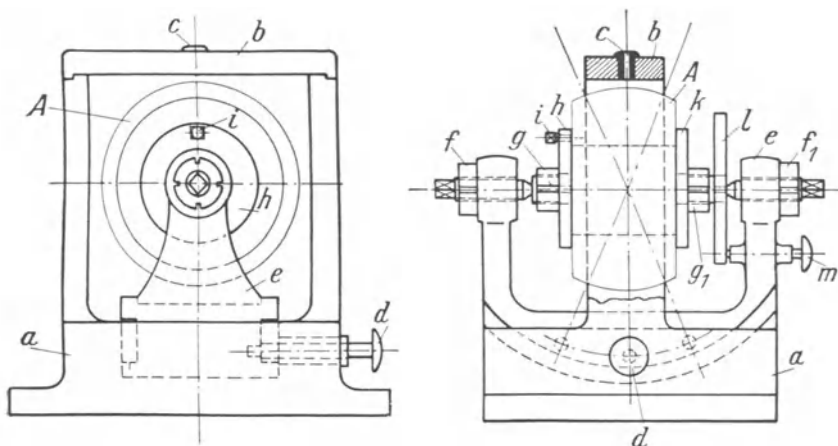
Bohrvorrichtung für kugelige Flächen.
